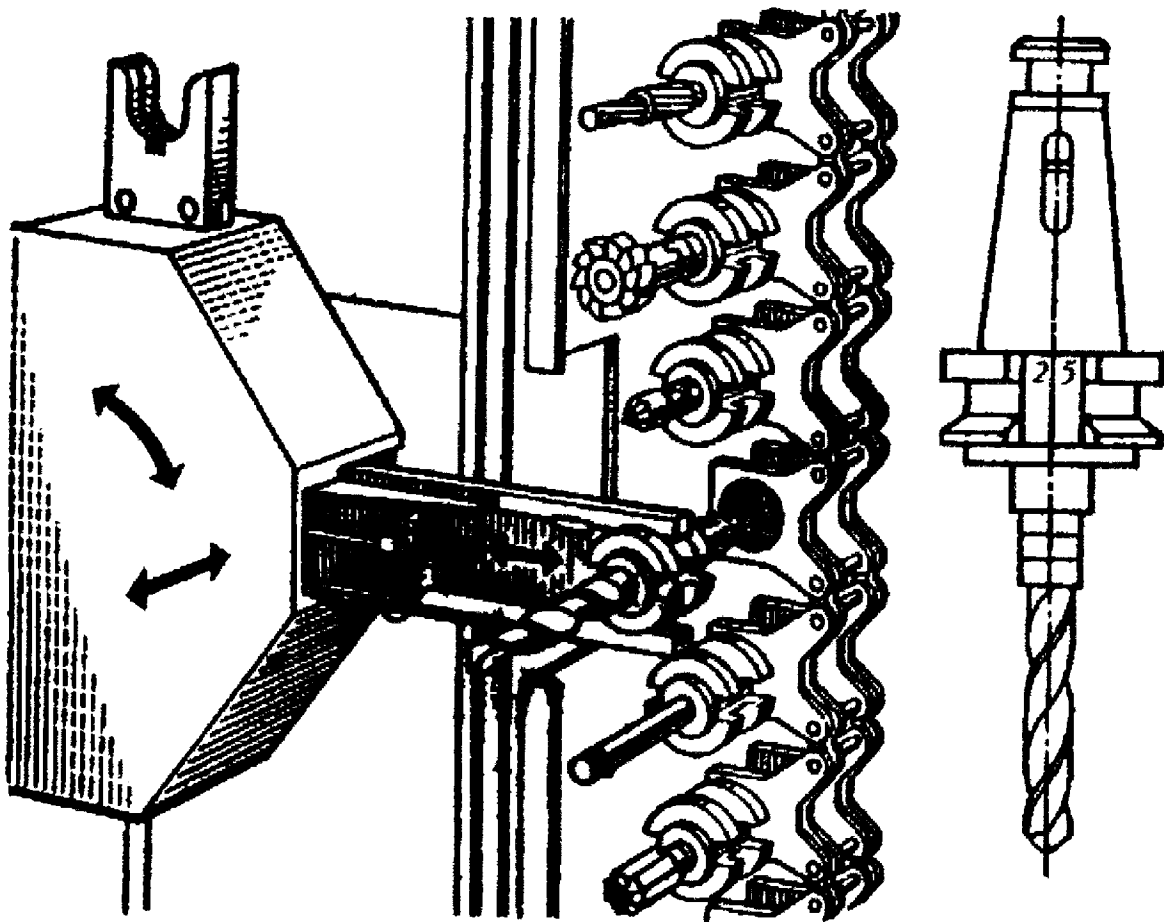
Инструменты, используемые при обработке корпусных деталей
